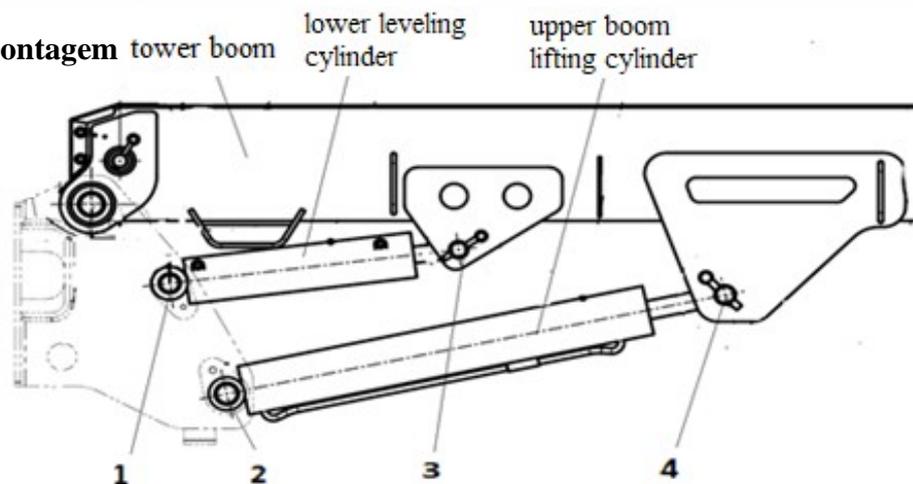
Diagrama de desmontagem do cilindro de elevação inferior e cilindro de elevação do braço
